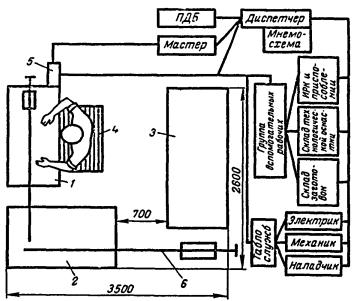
Планировка рабочего места сборщика при стендовой сборке:
